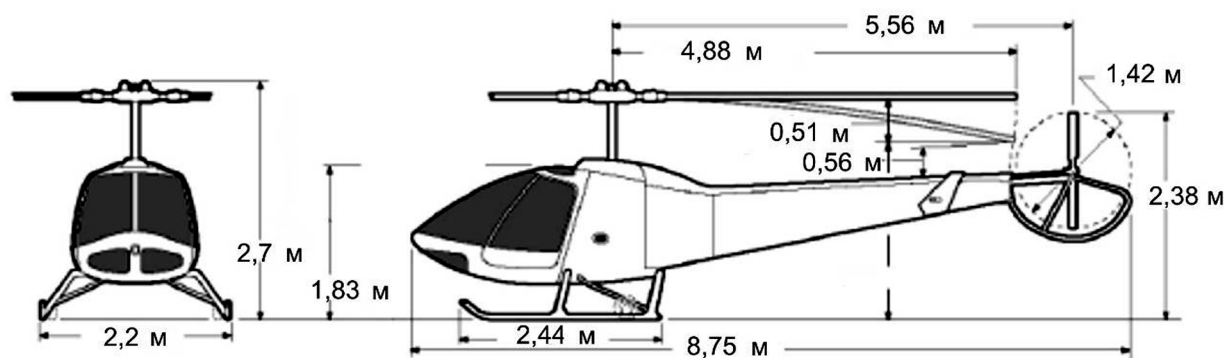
Схема вертолета Enstrom F-280F
